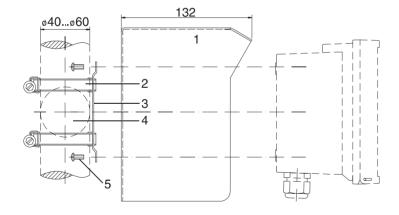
Kit ZU0274 de montagem em tubulação
